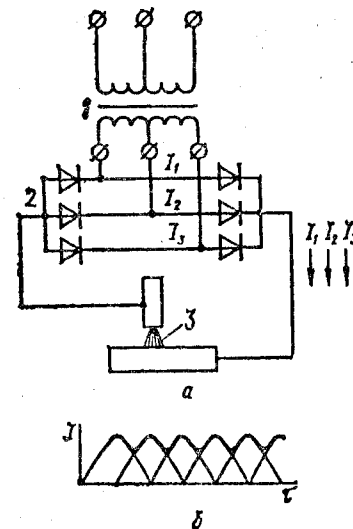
Схема трехфазного выпрямителя: а — схема включения; б — выпрямленный ток внешней цепи; 1 — понижающий трансформатор; 2 — блок селеновых или кремниевых выпрямителей; 3 — сварочная дуга
